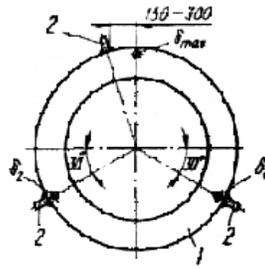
Схема установки сухарей и сборочных планок при сборке цилиндрических заготовок: 1 — торец свариваемой заготовки; 2 — соединительные планки;  $\delta_{max}$  — сухарь, имеющий наибольшую высоту;  $\delta_1 = \delta_2$  — сухари имеющие наименьшую высоту
